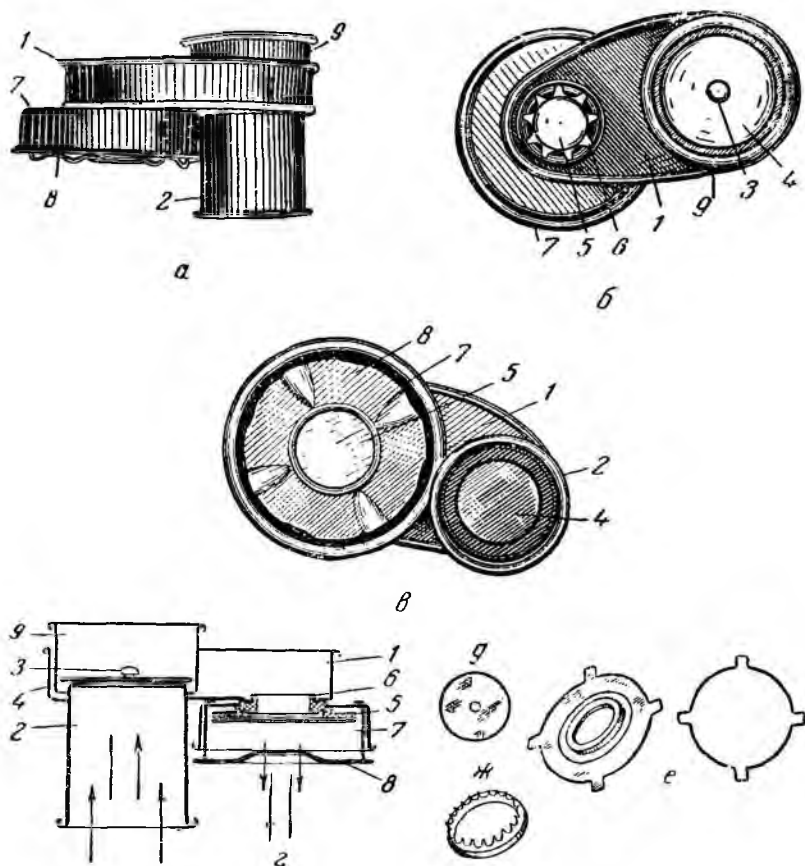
Клапанно-распределительная коробка-патрубок масок О-8 и Мод. О-8 (а — вид сбоку; б — вид сверху; в — вид снизу; з — боковой разрез; д — вдыхательный клапан; е — выдыхательный клапан; ж — зубчатая муфта; (стрелки на чертеже показывают движение воздуха):
